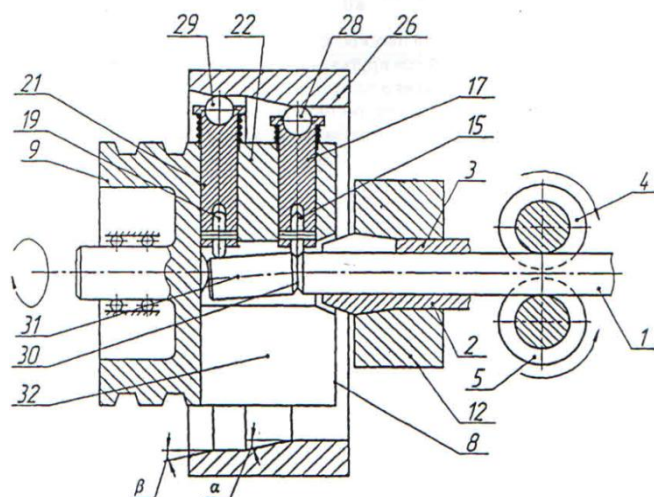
Положение штампа в момент отделения мерной заготовки от прутка
